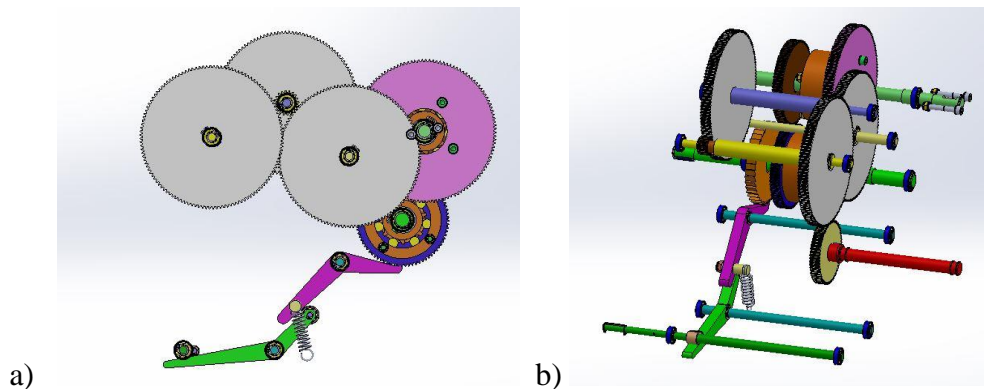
a) Escada de engrenagens dimensionada b) Veios de acoplamento de engrenagens
